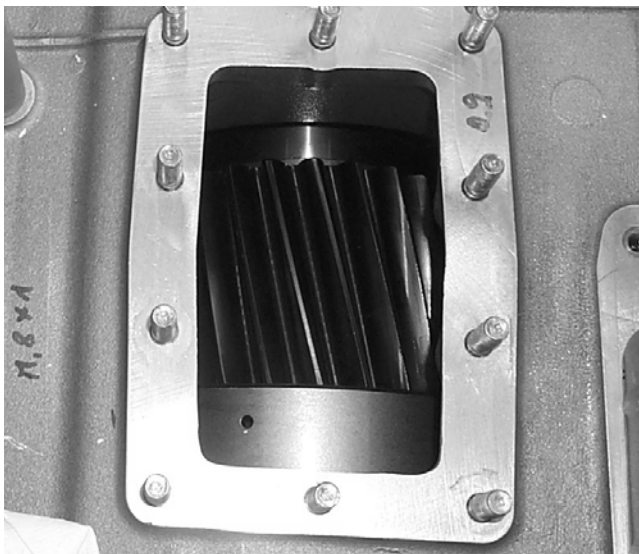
Blick auf die Verzahnung (Getriebe ZF 3000, Beispiel)
